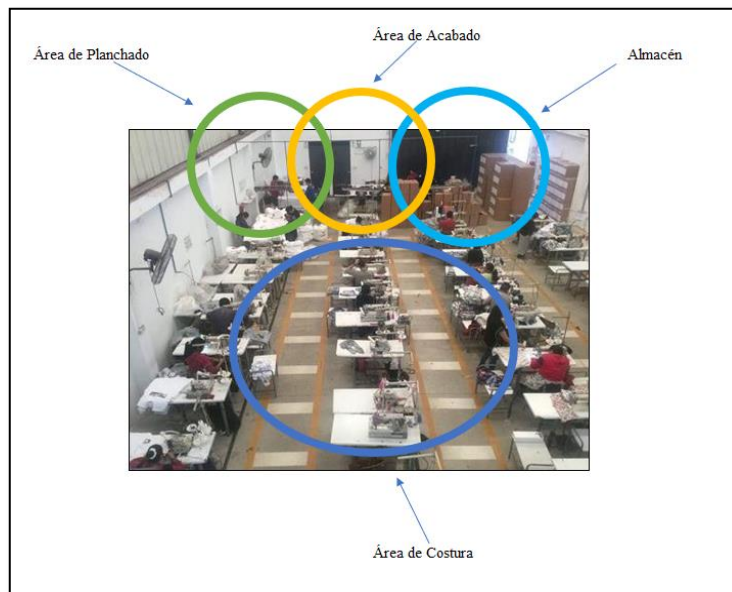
Solapamiento de las áreas de trabajo dentro de la planta
